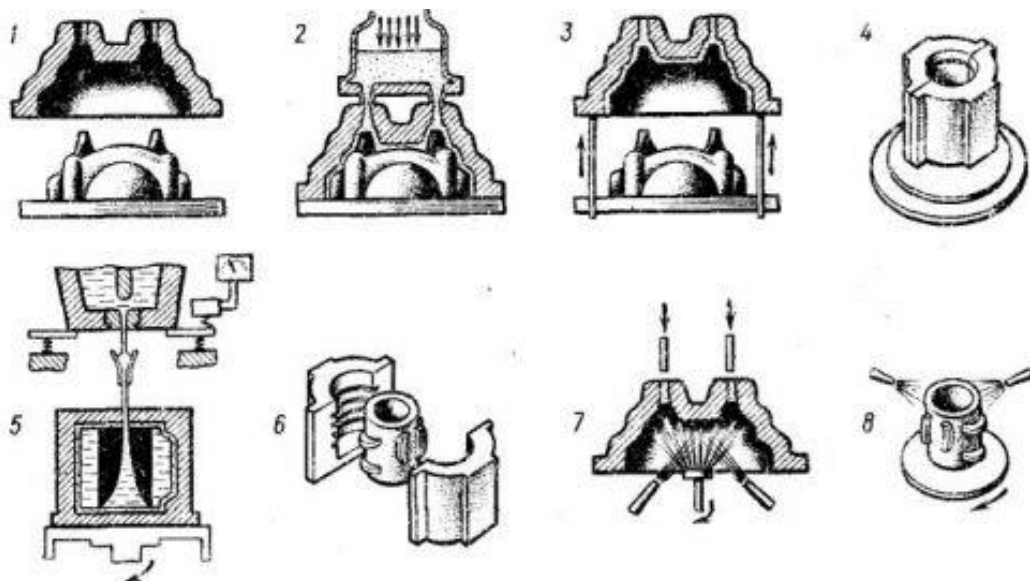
Схема технологического процесса отливки корпуса буксы в кокиль центробежным методом
